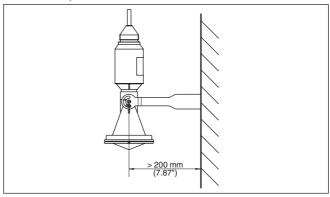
Montaggio a parete tramite la staffa di montaggio lunga 170 mm
